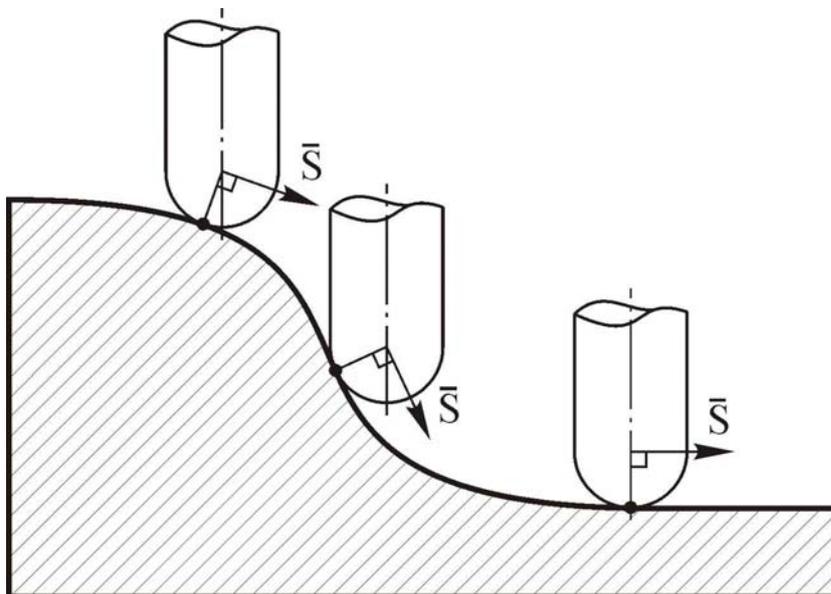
Смещение точки контакта заготовки и фрезы вдоль ее криволинейной режущей кромки
